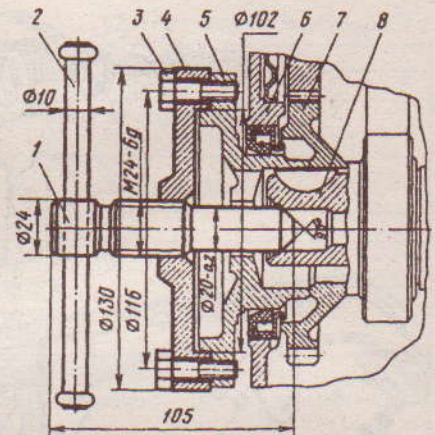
Съемник для снятия центробежного маслоочистителя: 1 – винт съемника в сборе с воротком; 2 – корпус съемника; 3 – коленчатый вал; 4 – шестерня
